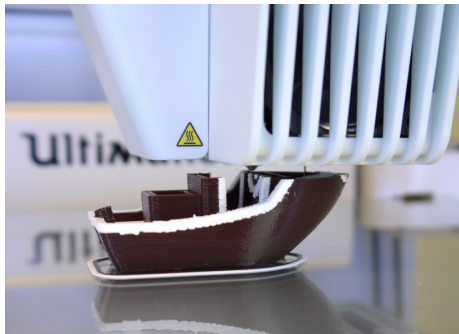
Impresión FDM en impresora ULTIMAKER 3 [22].
